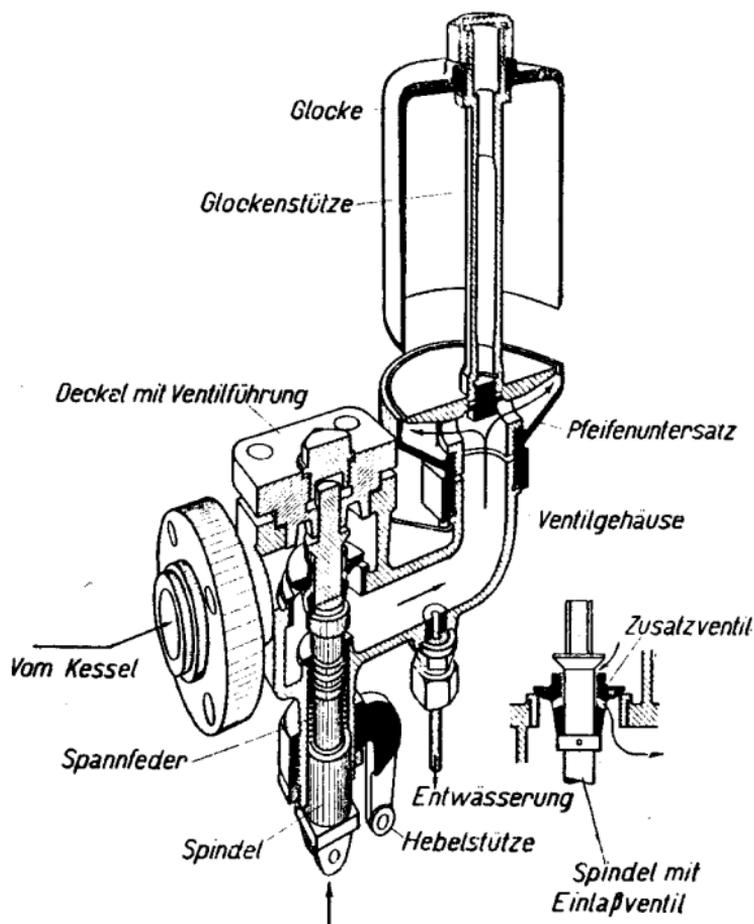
Schnitt durch Ventilgehäuse und Glocke
